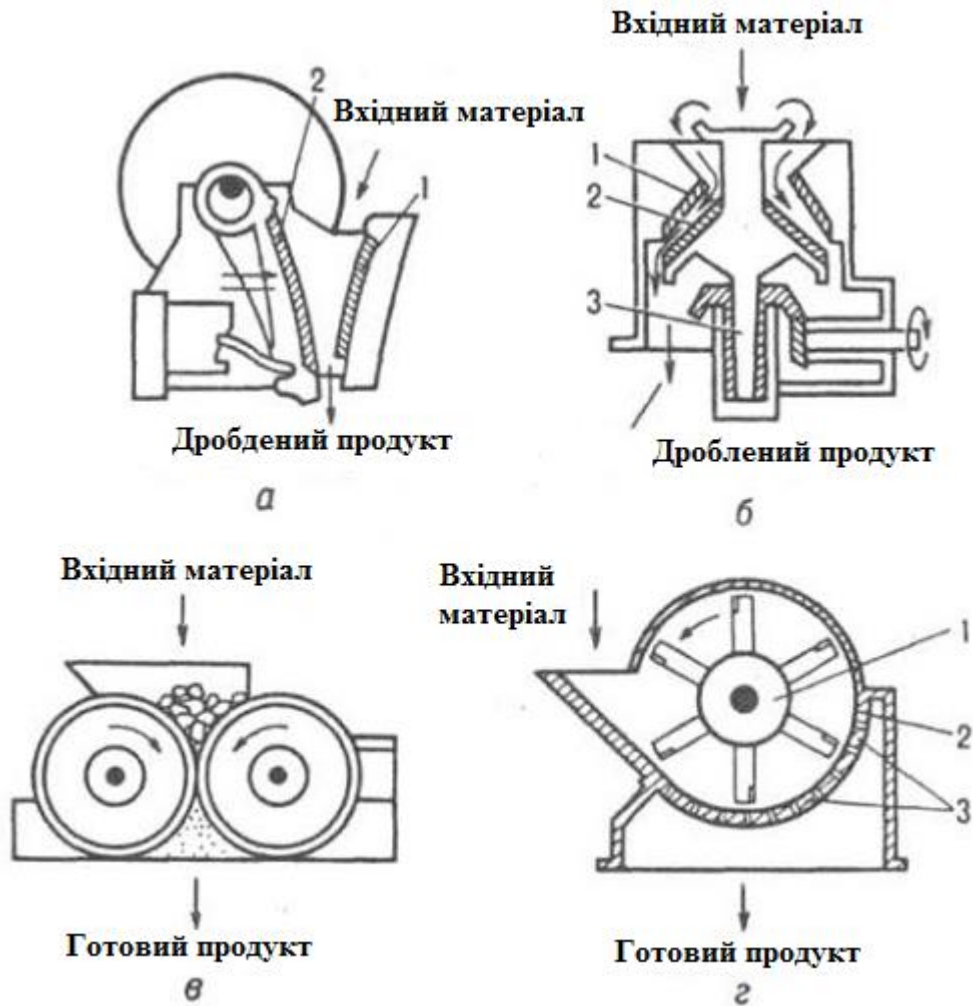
Основні типи дробарок: а - щокова (1, 2 - нерухома і рухома щоки); б - конусна (1, 2 - нерухомий і хитний конуси, 3 - вал); в - валкова; г - роторна (1 - ротор з молотками, 2 - статор, 3 - колосники)
